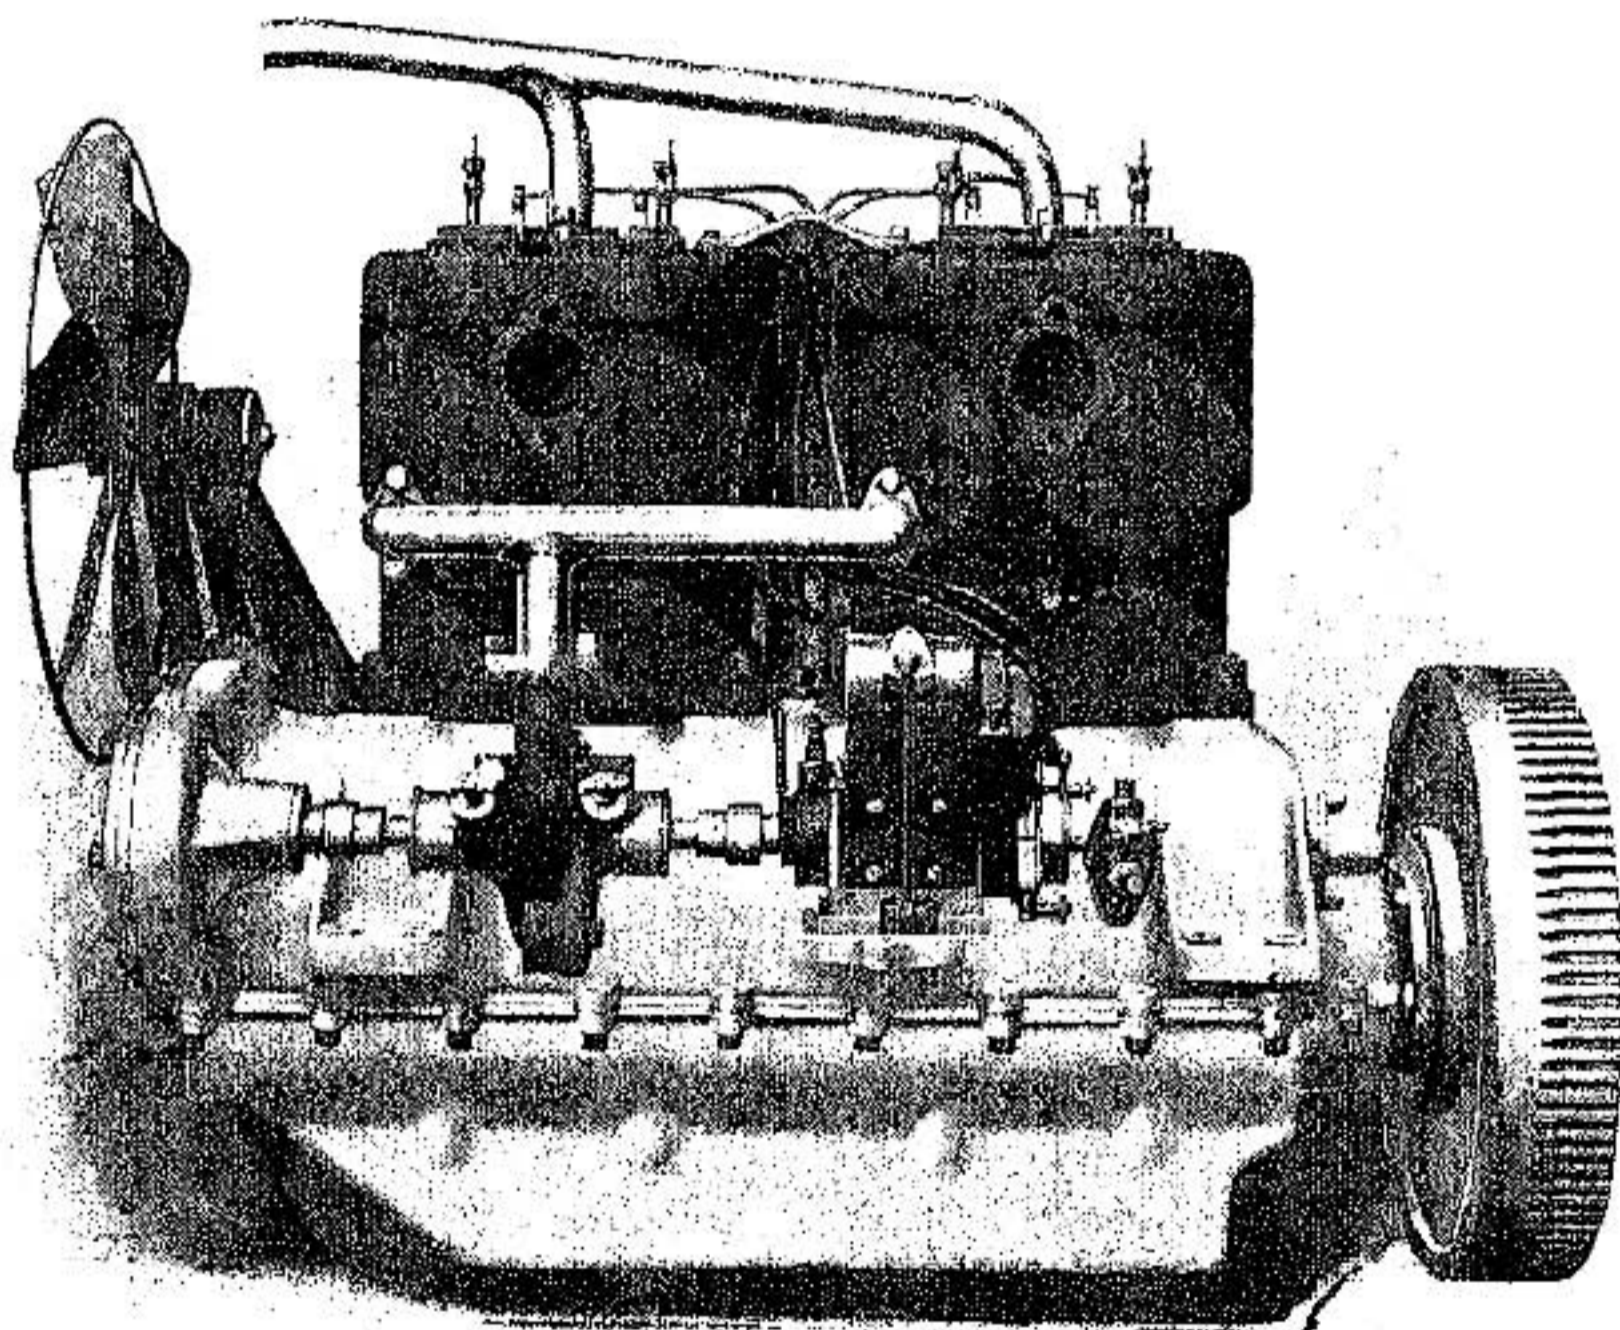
Двигатель Кейсъ 40 HP со стороны выпуска.
